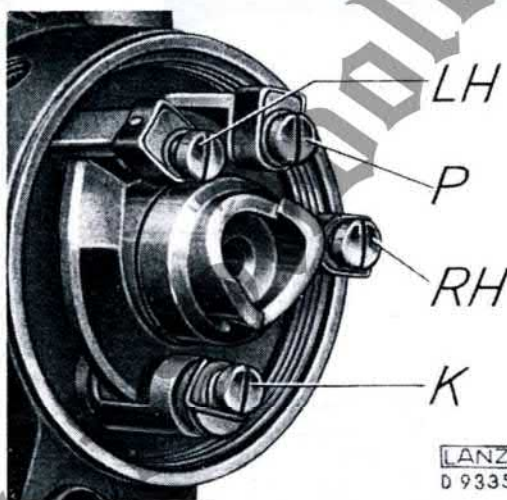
Schlitzschrauben für Ölpumpen d. Boschölers
